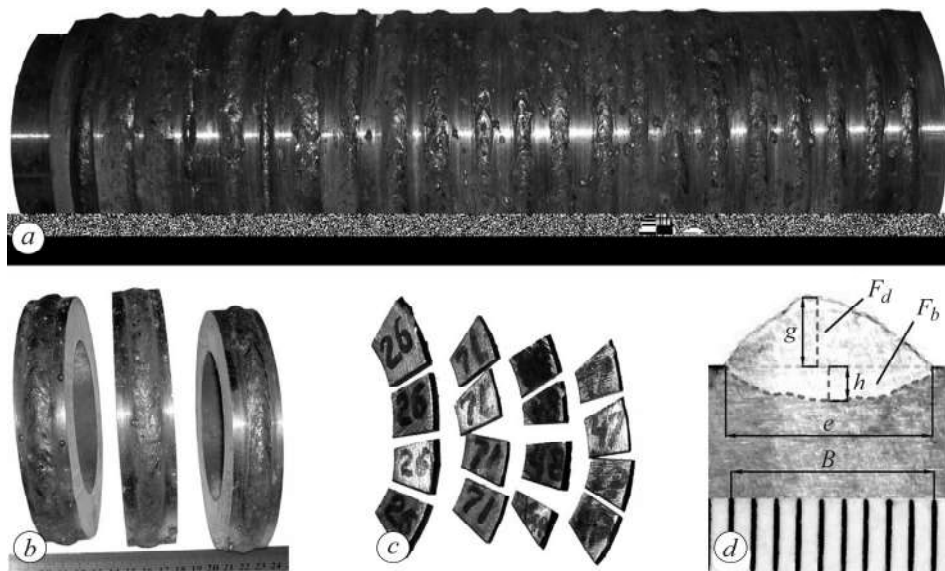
Етапи виготовлення макрошліфів: *a, b* – циліндрична заготовка після наплавлення та розрізання; *c, d* – вирізані сегменти та підготовлений макрошліф.
